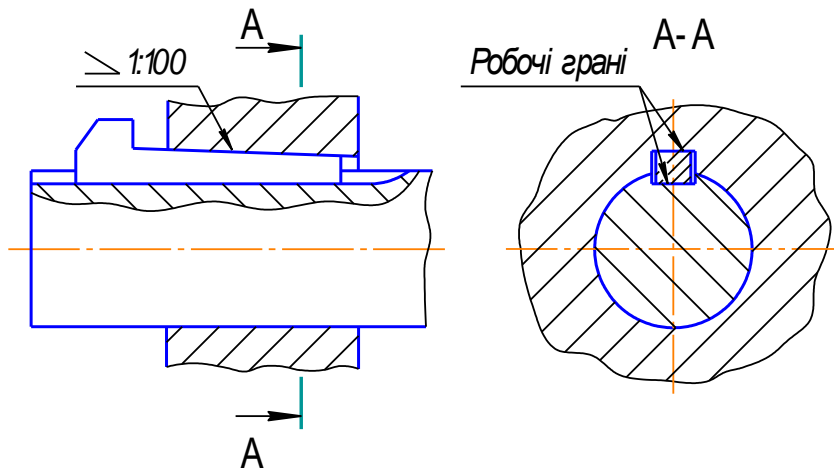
Конструкція шпонкового з'єднання з клиновою шпонкою
